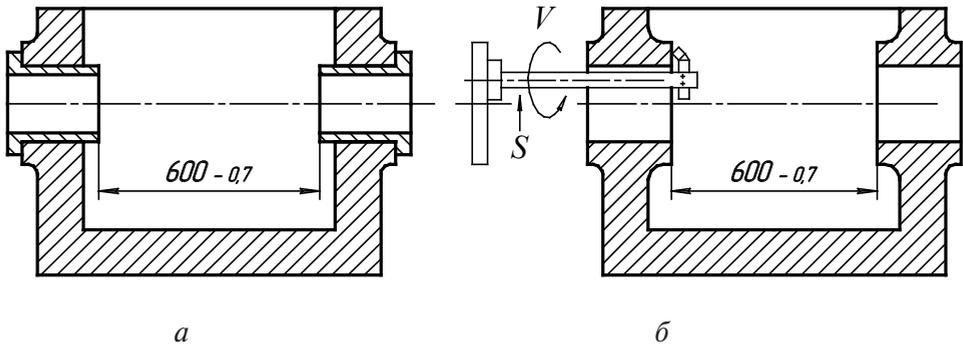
Конструкция корпусных деталей с точным размером между внутренними торцами отверстий:
